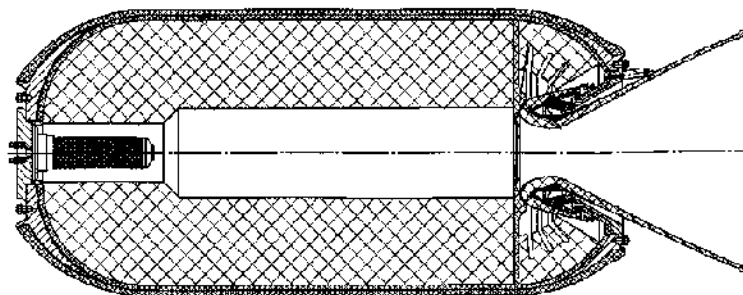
Ракетный двигатель твердого топлива с утопленным соплом
